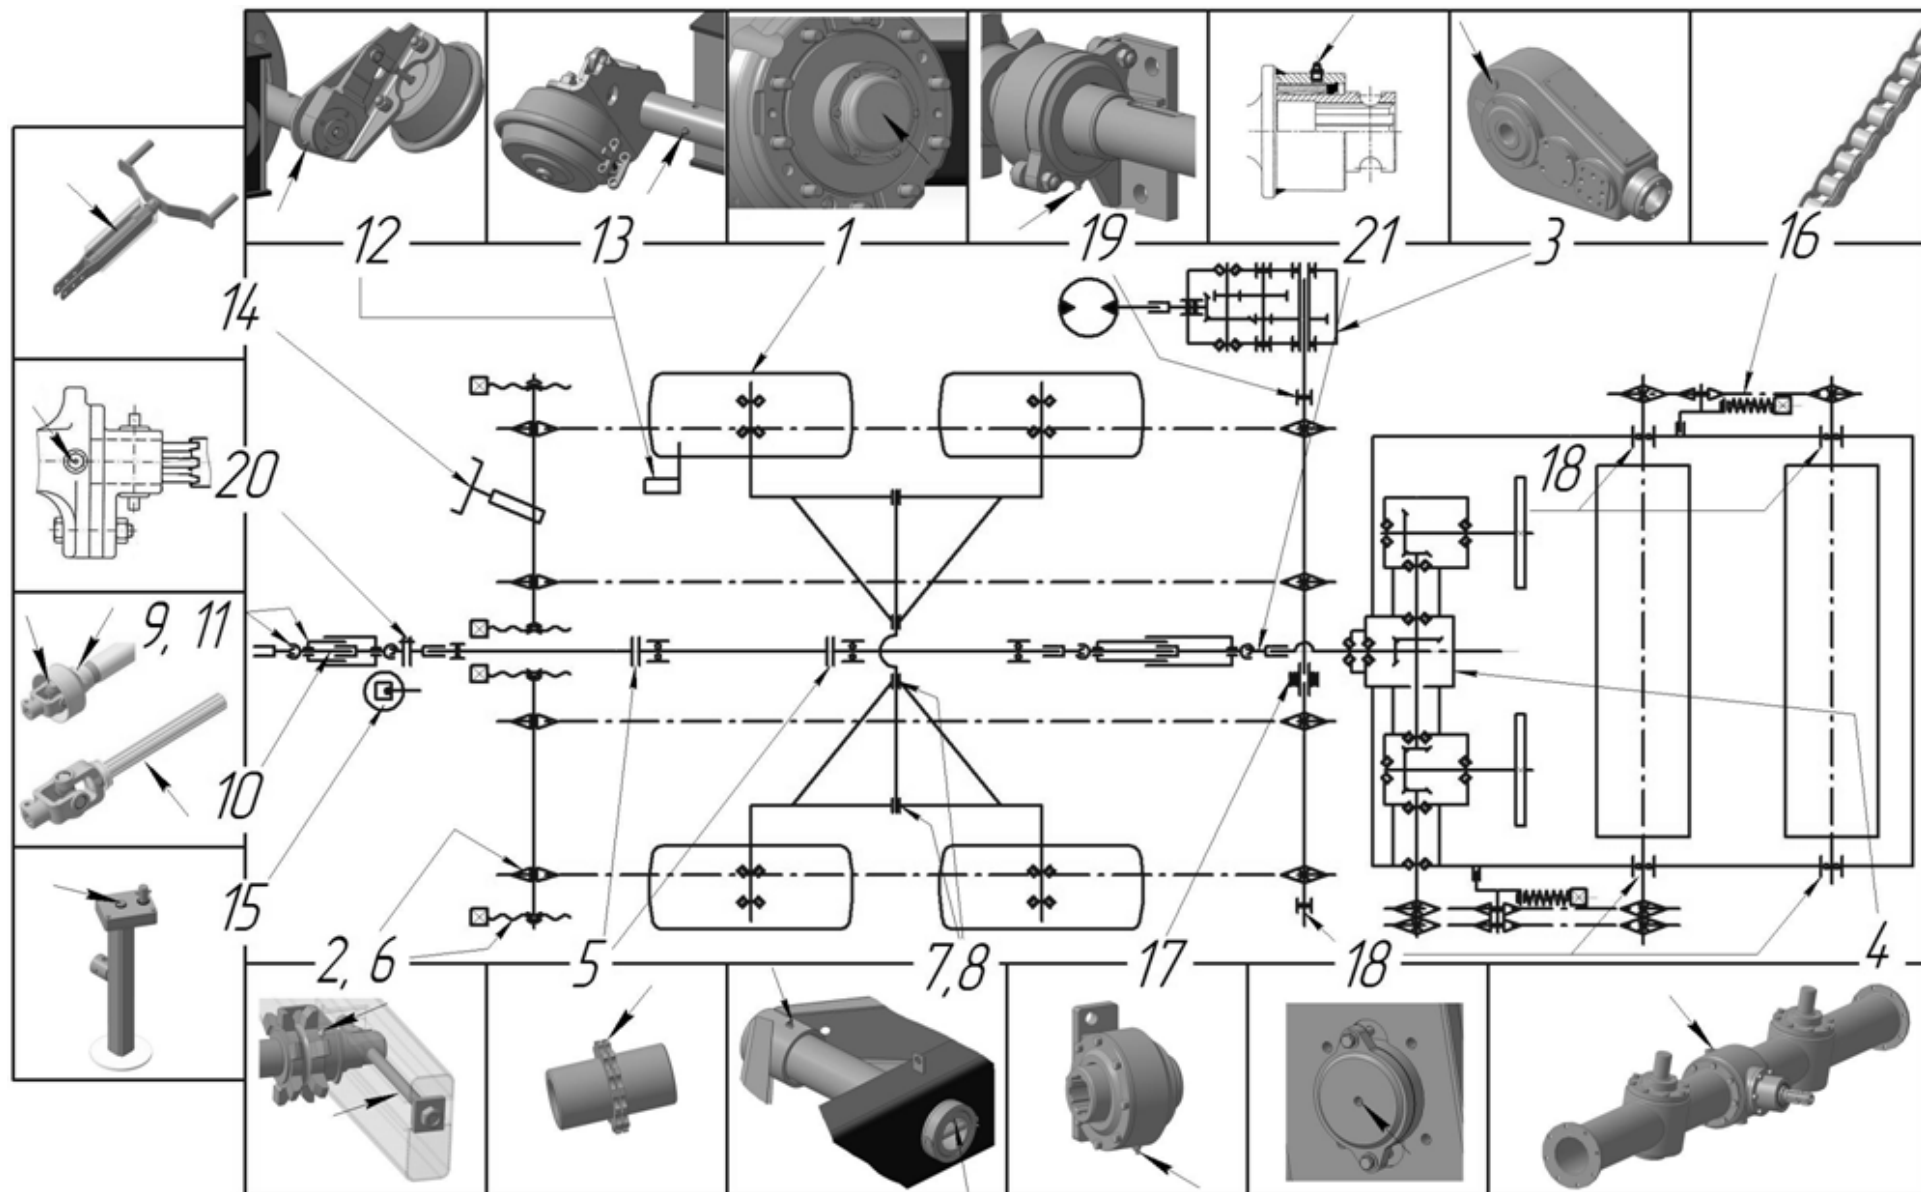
Схема смазки (машина с разбрасывателем с двумя горизонтальными барабанами)
